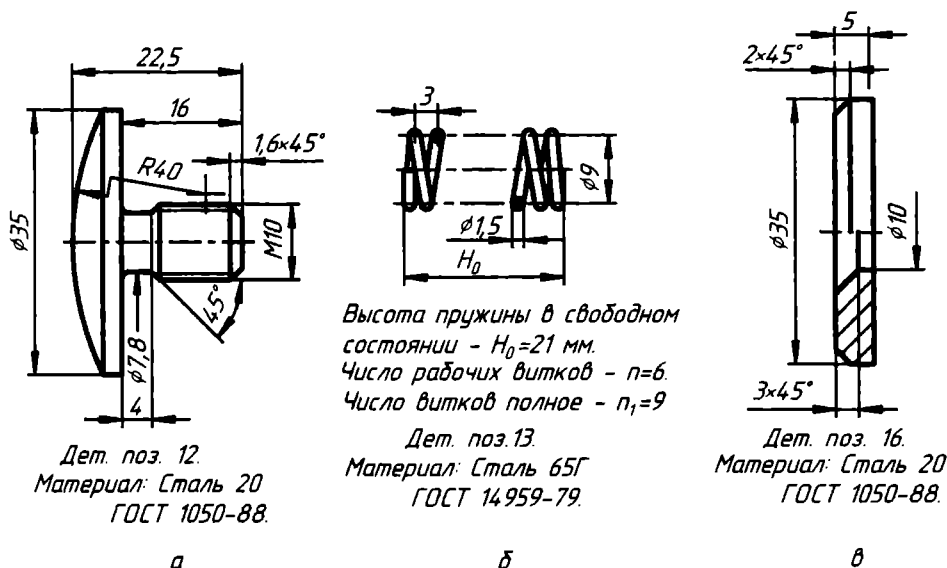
Чертежи: а — головки; б — пружины; в — шайбы
